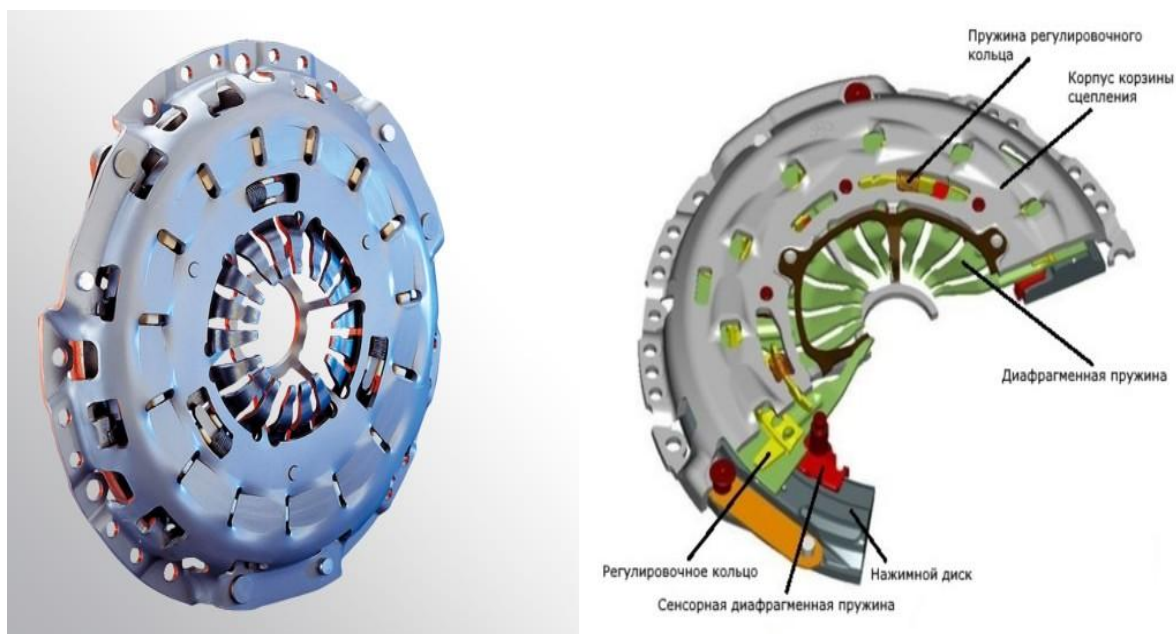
Общий вид и элементы конструкции саморегулирующегося сцепления SAC
